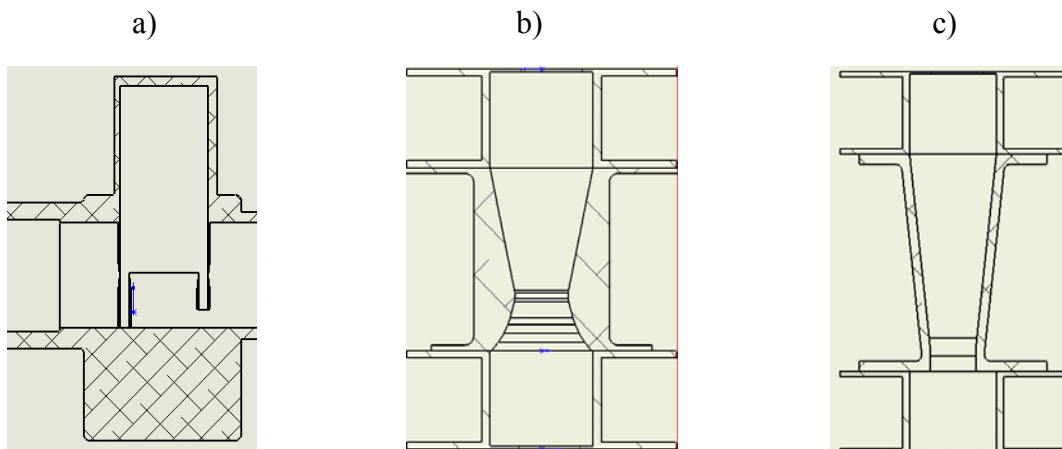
a) Sezione Valvola Piatta, b) Sezione Complessivo R. Lucido, c) Sezione Complessivo R. Grezzo
